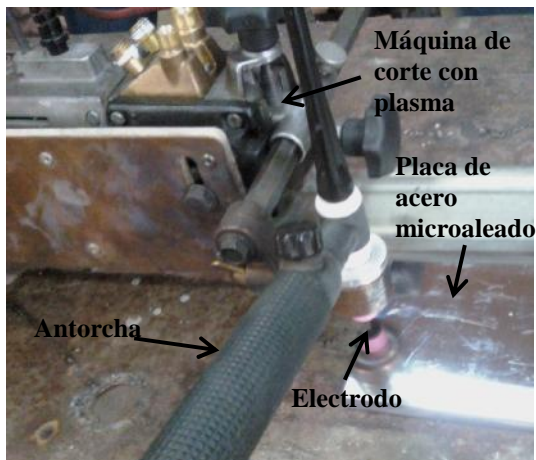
Antorcha de la soldadora de proceso GTAW adaptada a una máquina de corte con plasma.
